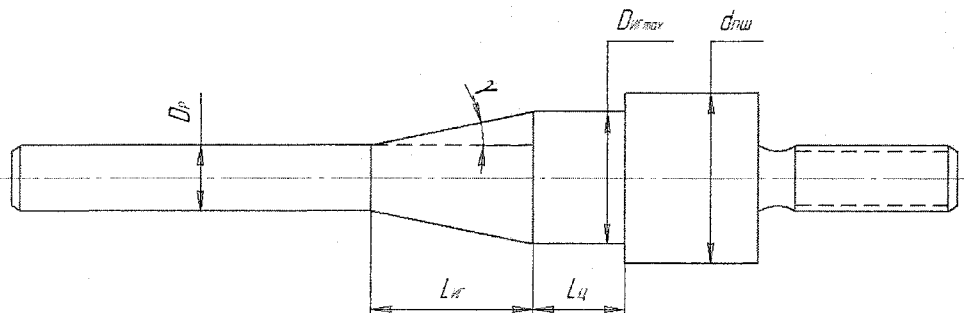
Профилировка рабочей поверхности пресс-иглы: D_p – диаметр цилиндрического участка, обеспечивающего получение трубы с номинальной стенкой, мм; $L_{кр}$ – длина конического участка иглы, обеспечивающего плавное уменьшение стенки на заднем конце прессованной трубы, мм; $L_{ц}$ – цилиндрический участок, мм; $D_{иг. макс}$ – больший диаметр конического участка пресс-иглы, мм; $d_{пш}$ – диаметр под пресс-шайбу, мм; γ – угол конусности конического участка, град
